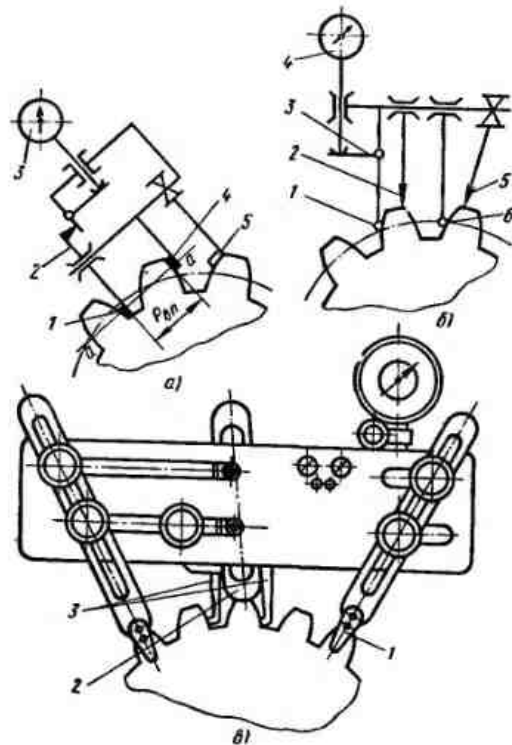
Схемы (а, б) и конструкция (в) накладных шагомеров
